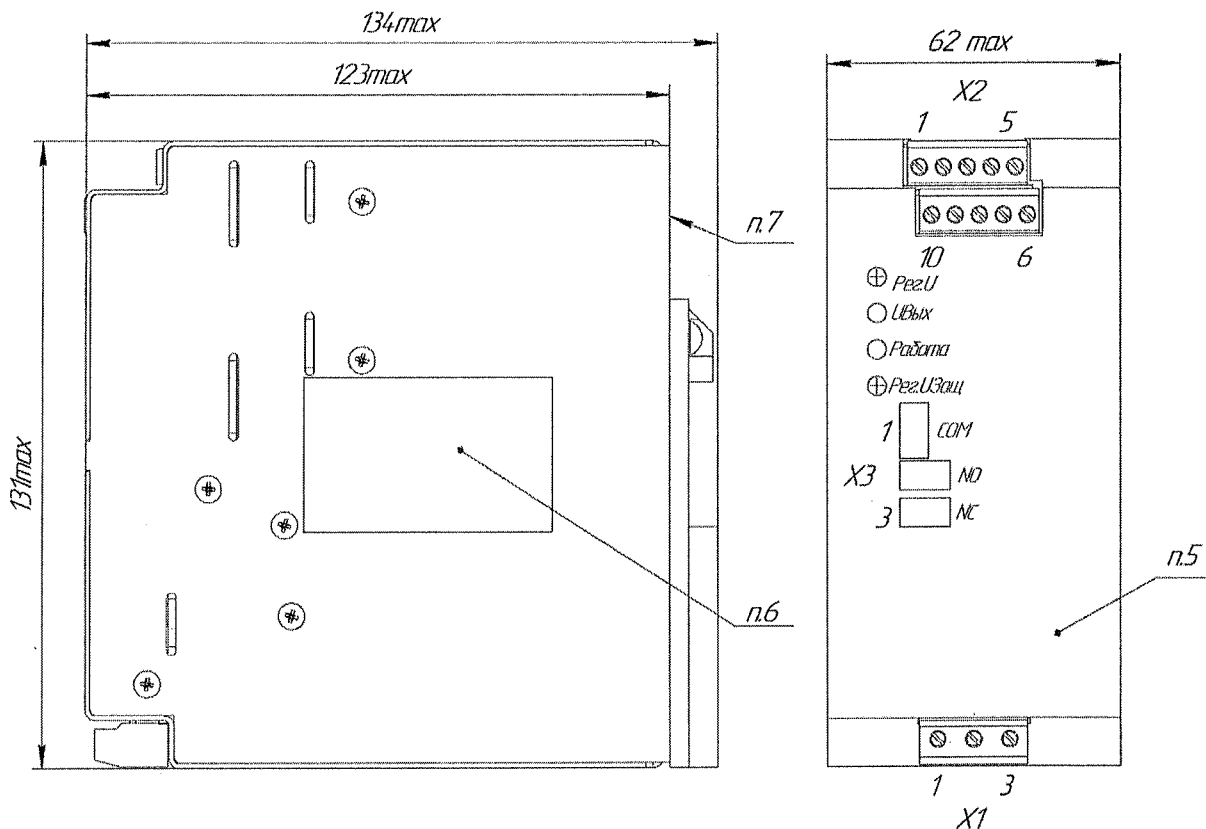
Габаритные размеры модуля КАН-Д300
